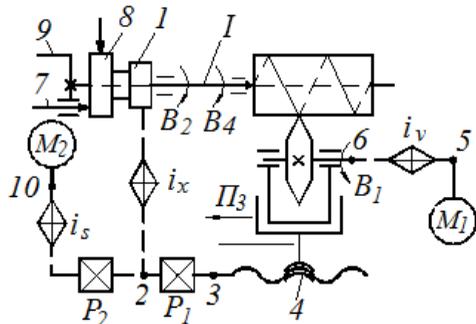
Кинематическая структура резьбофрезерного станка с последовательным соединением кинематических групп
